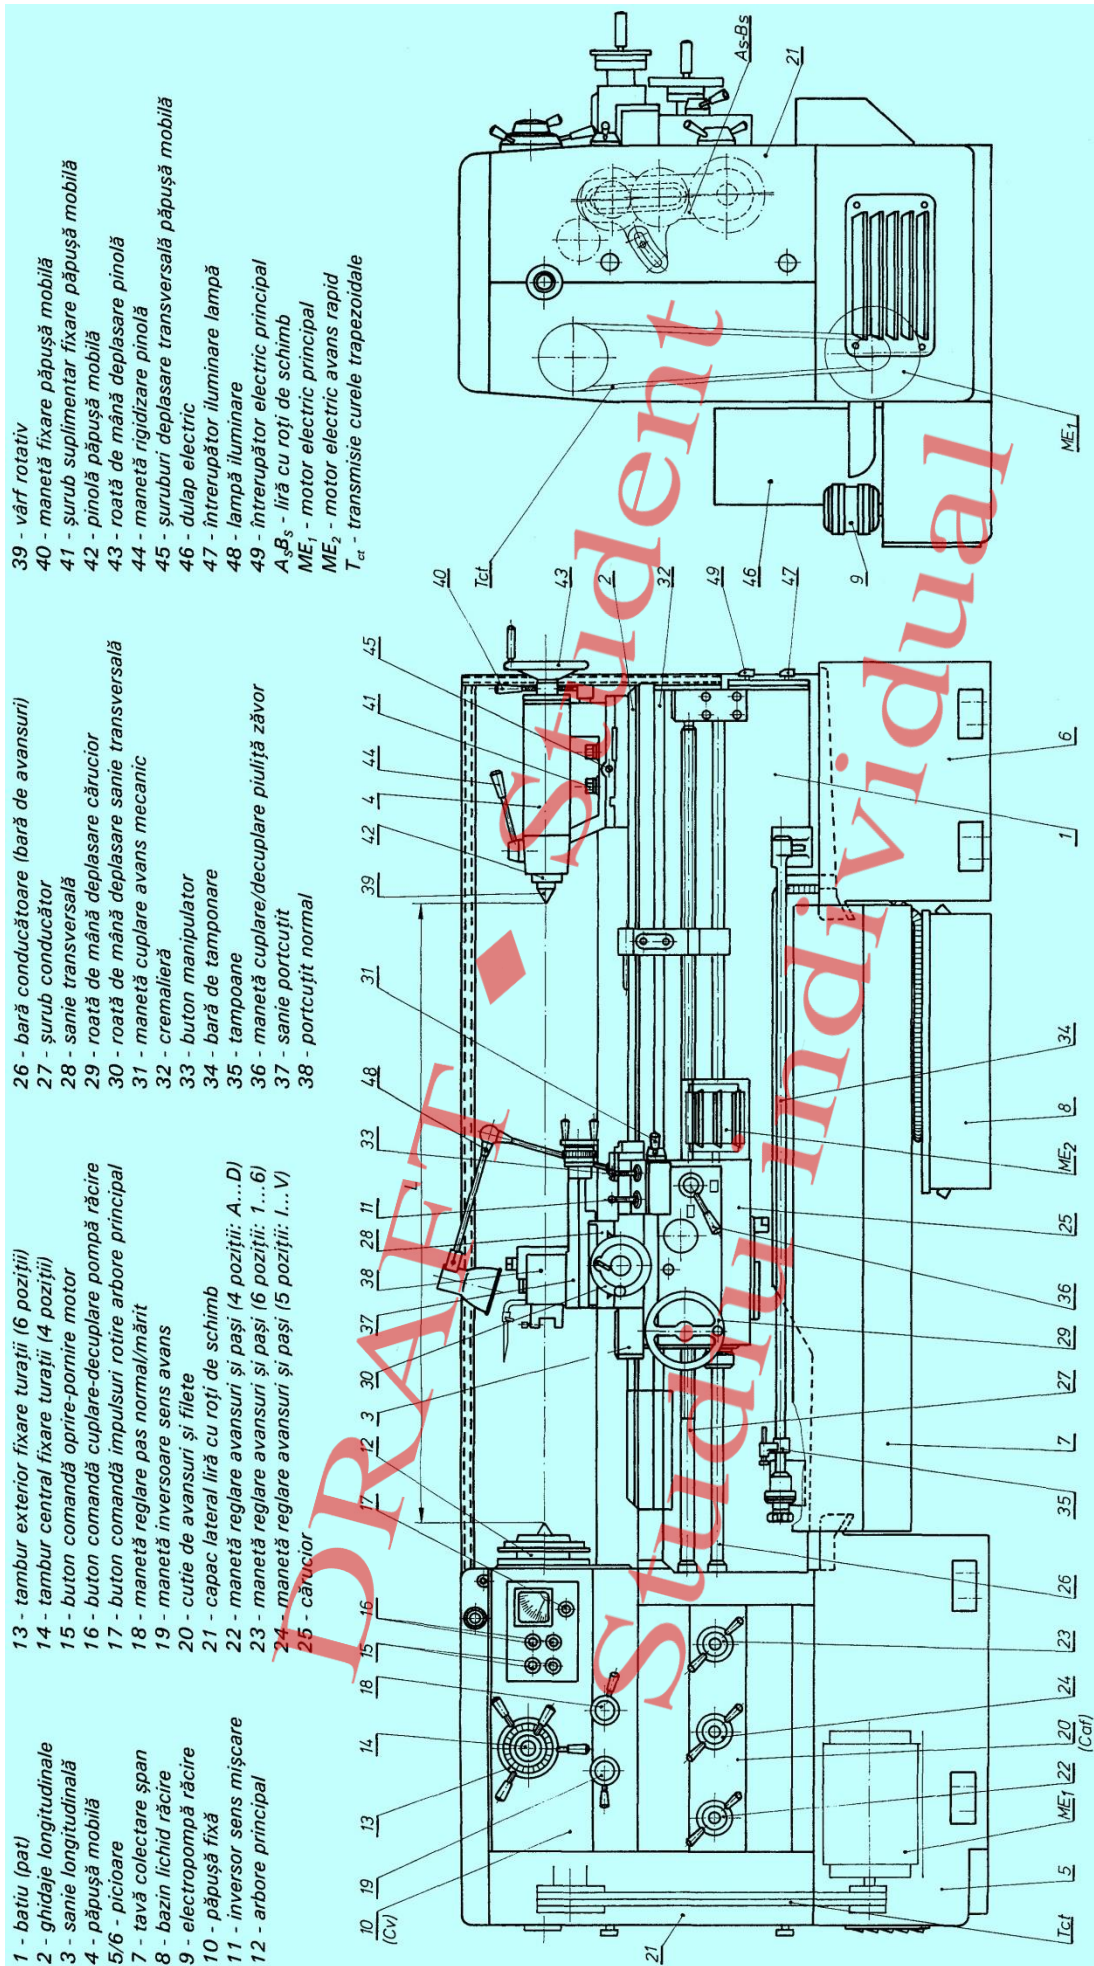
Elementele constructive ale strungului normal SNA-500
